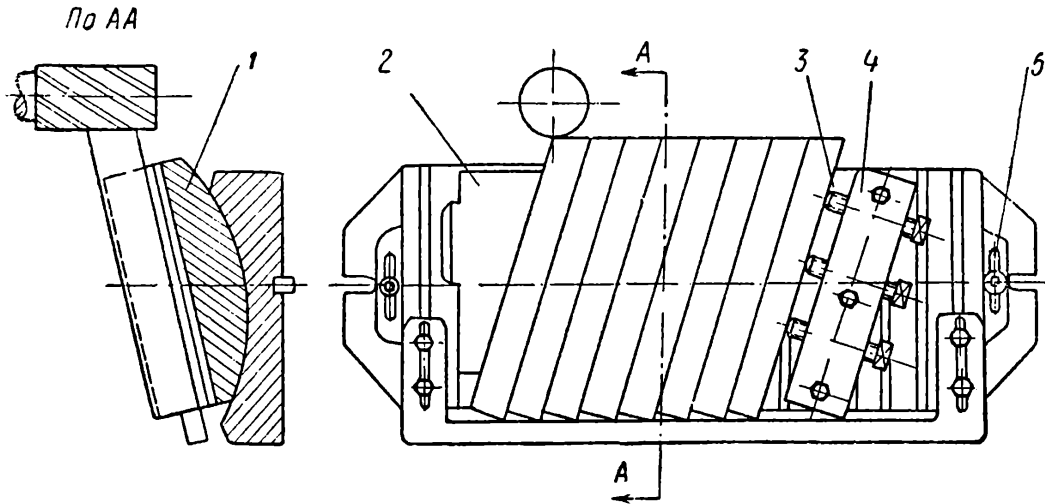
Приспособление для фрезерования главной задней грани прямых резцов на горизонтально-фрезерном станке.
